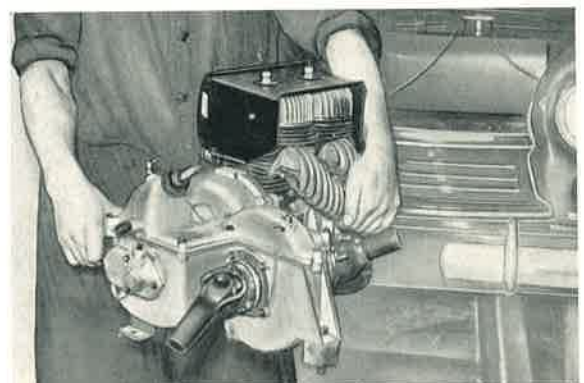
So wird der aus dem Motor-Raum herausgehobene Motor bequem von einem Mann getragen.
